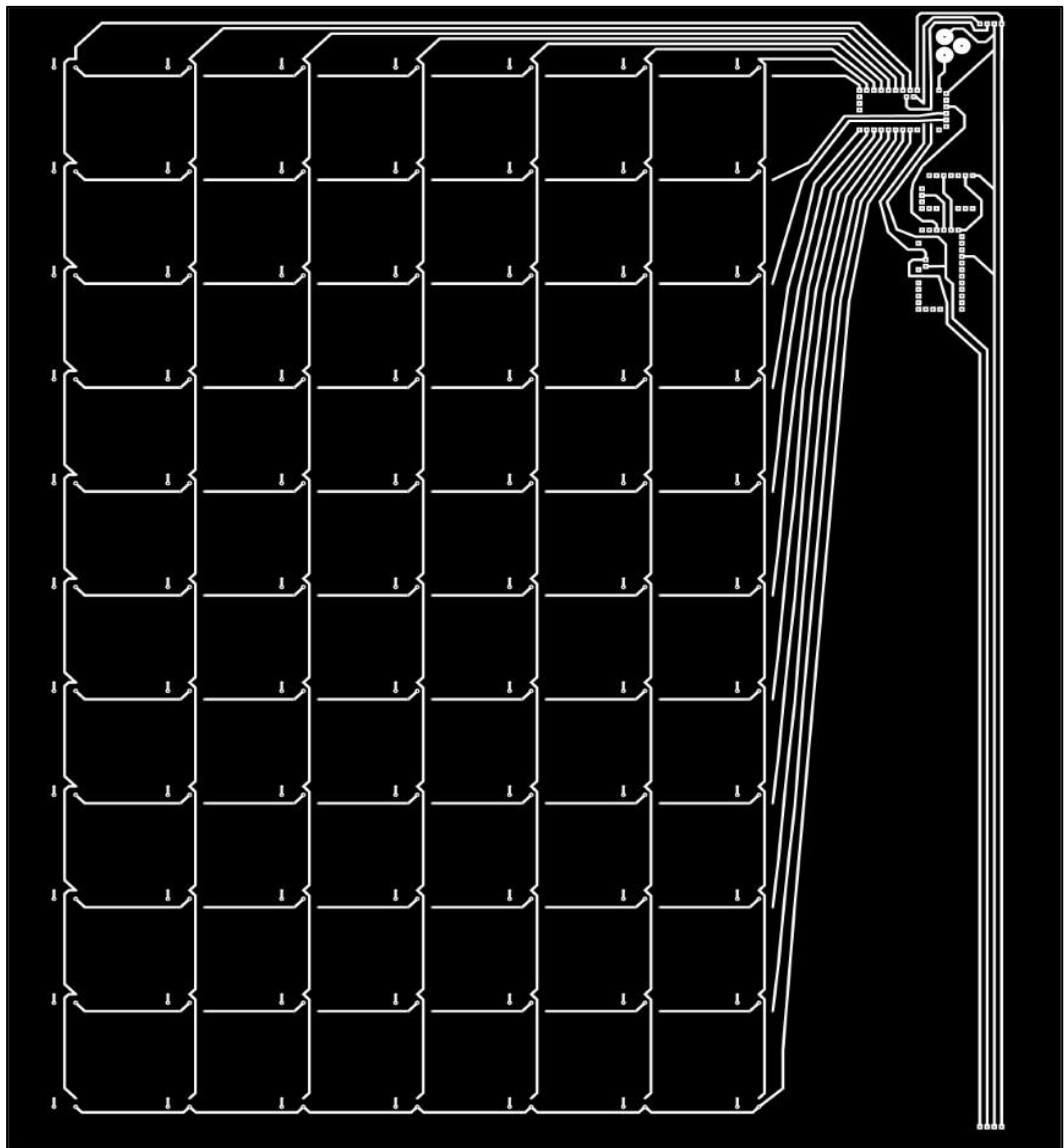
Aspecto final do layout do esquema eletrônico para impressão e montagem da PCI.
